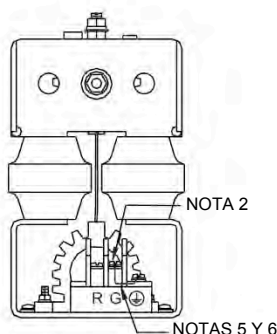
SE-MRE-600 con el ER-600VC instalado.
